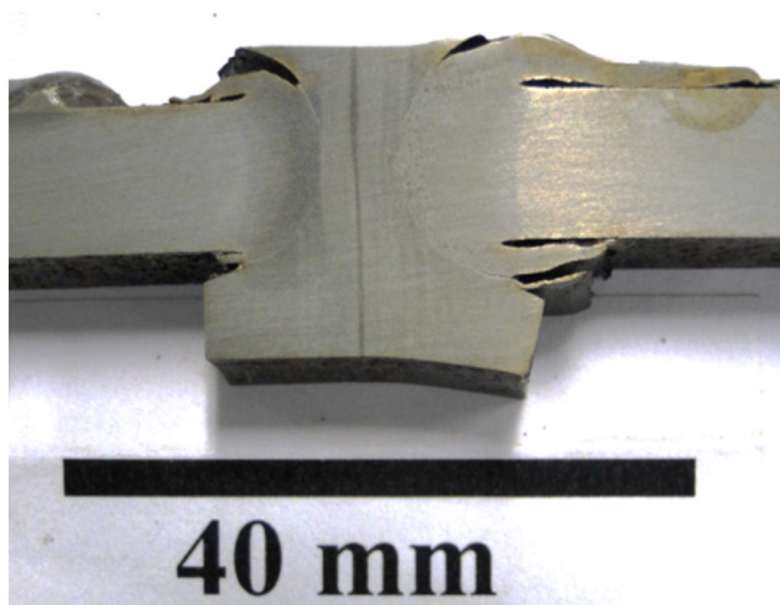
Diferenças entre as rebarbas na soldagem entre tubo-anel-tubo.
